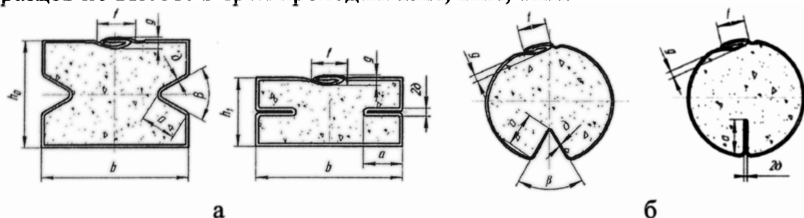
Поперечное сечение образцов порошковой проволоки до и после прокатки: а - плоский образец, б - круглый образец
